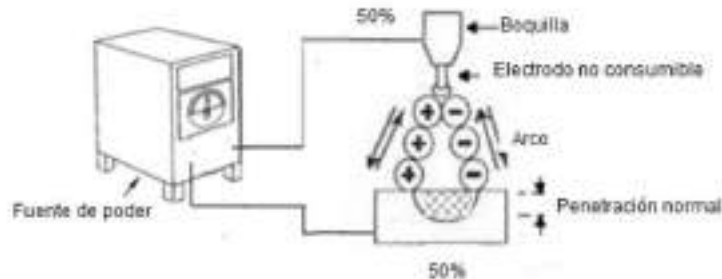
Efectos de la corriente alterna en el cordón de soldadura.
